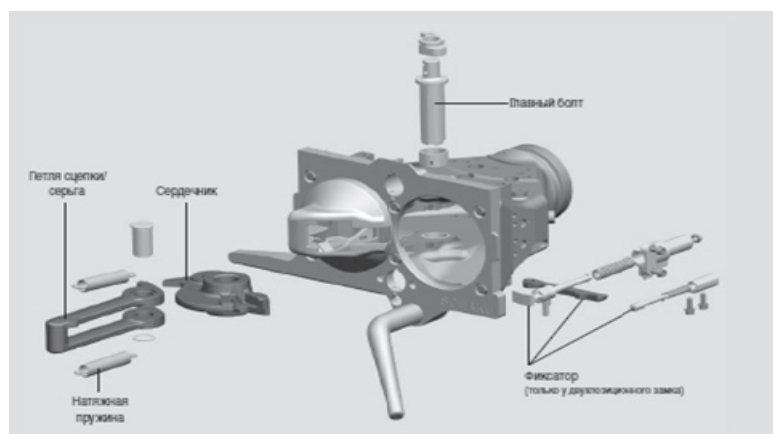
Сборочный чертеж головки сцепного устройства с замком сцепления
